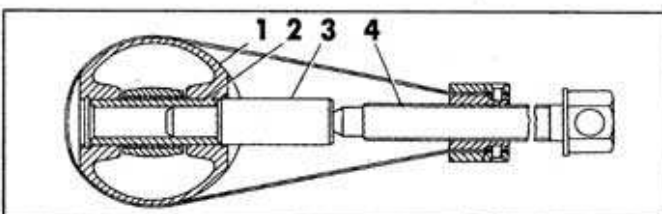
Выпрессовка поршневого пальца из поршня съемником 7823-6102:
